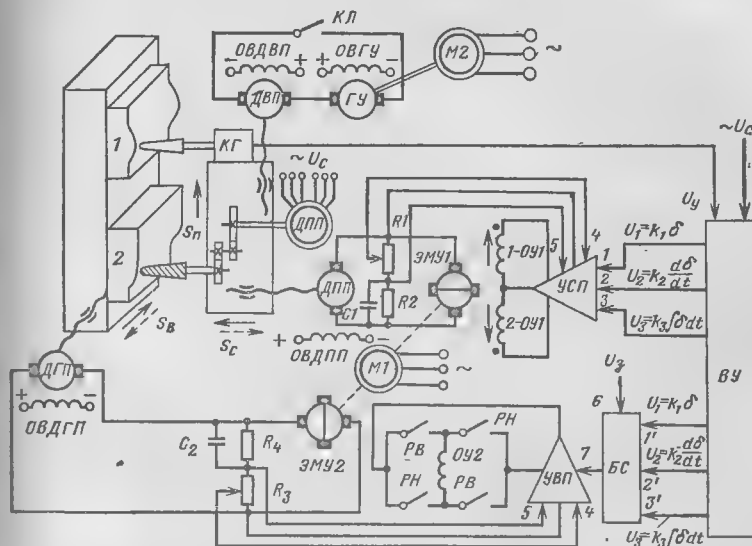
Схема управления электроприводами копировально-фрезерного станка 644Б.
